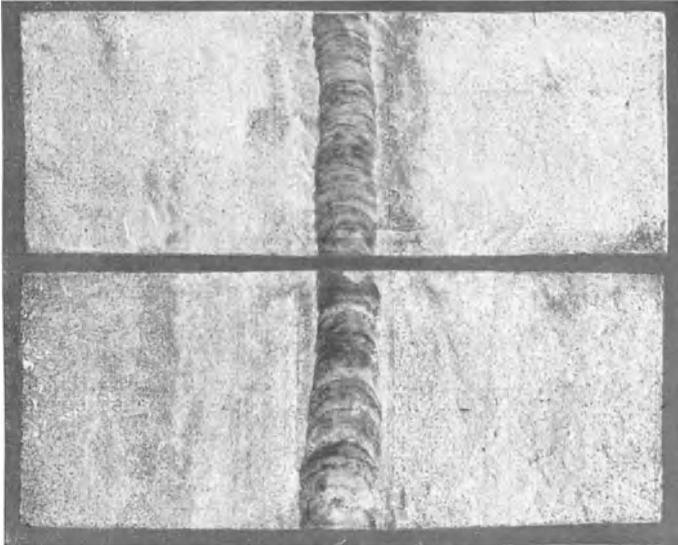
Längsschliffe der Schweißnaht von Aluminiumblech.
